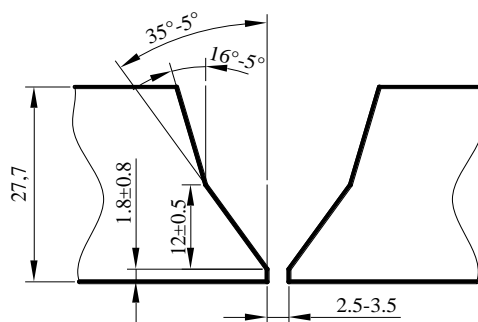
Подготовка кромок труб под сварку
